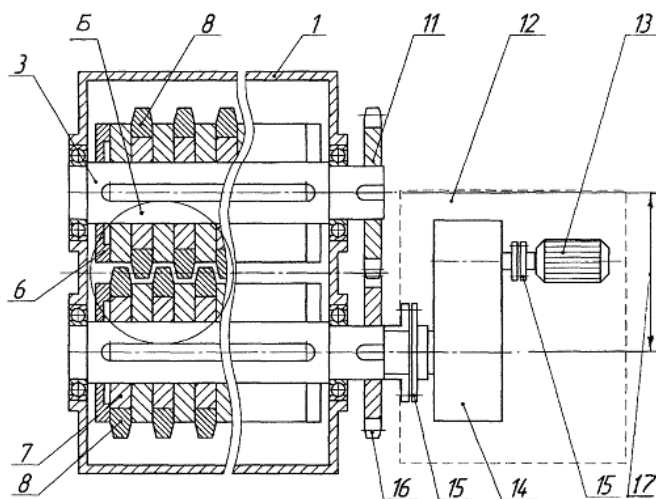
Схема горизонтального розрізу валкової дробарки
